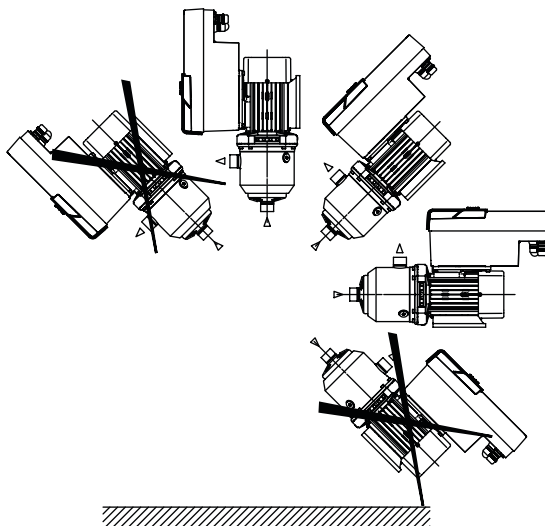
Godkjente monteringsstillinger med motoraksel og elektronikkmodulen oppover (0°)
